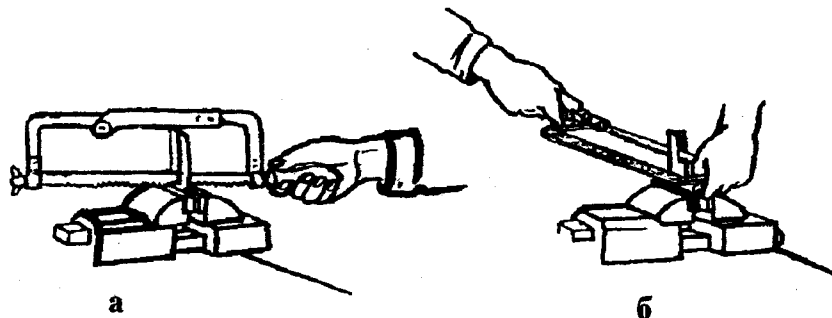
Резка ножовкой: а — без поворота полотна; б — с поворотом полотна на 90°
